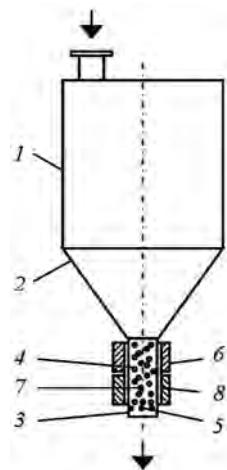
Живильник сипкого матеріалу [18]: 1 — вертикальний циліндричний бункер; 2 — конічне днище; 3 — випускний патрубок; 4, 7 — феромагнітні тіла; 5 — сітка; 6 — електромагніт; 8 — котушка індуктивності.
